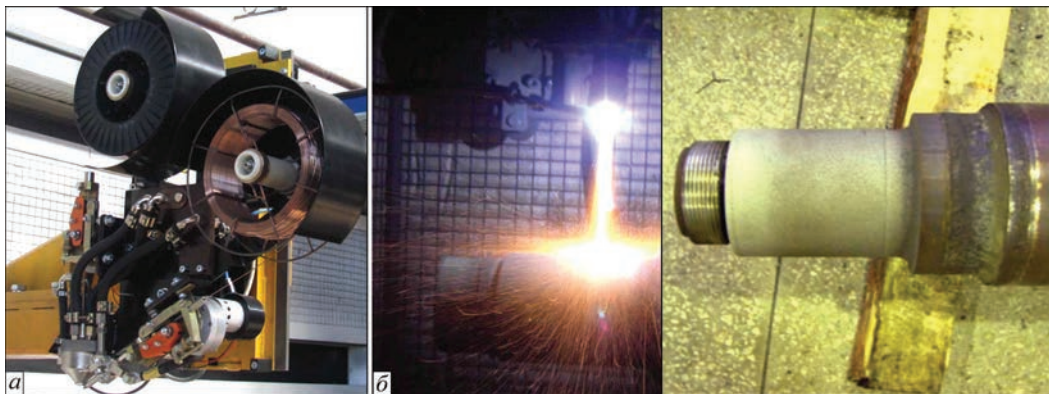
Внешний вид блока машинного сверхзвукового металлатора PLAZER15-SAEM установки PLAZER15-SA (а), процесс напыления с его помощью износостойких покрытий из порошковых проволок на основе Fe–Cr–C на шейки осей колесных пар железнодорожного транспорта (б)
